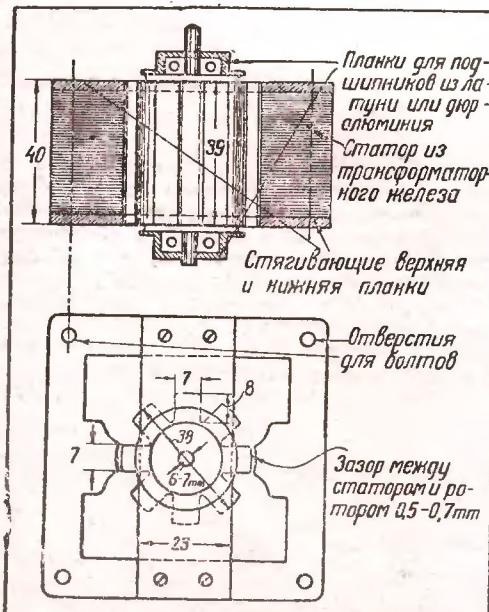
Ротор и статор мотора — вид сбоку и сверху
